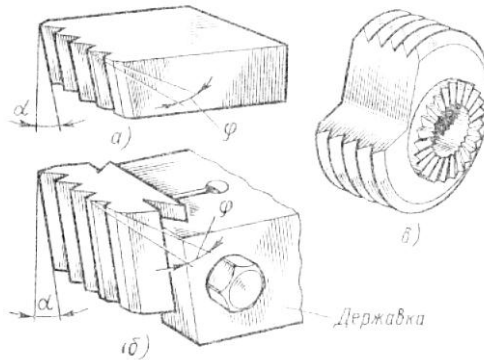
Резьбовые гребёнки: а-стержневая; б-призматическая; в-круглая
